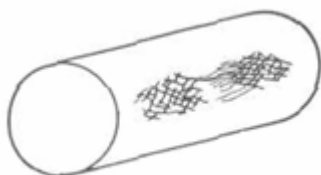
Схема прутка стали с сеткой шлифовочных трещин
